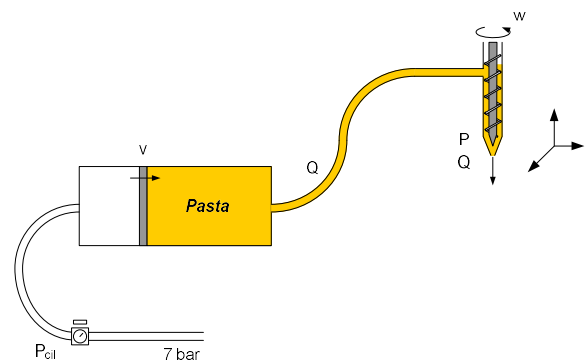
Esquema de funcionamento da impressora de *robocasting
